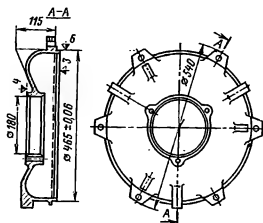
Подшипниковый щит асинхронного двигателя.
